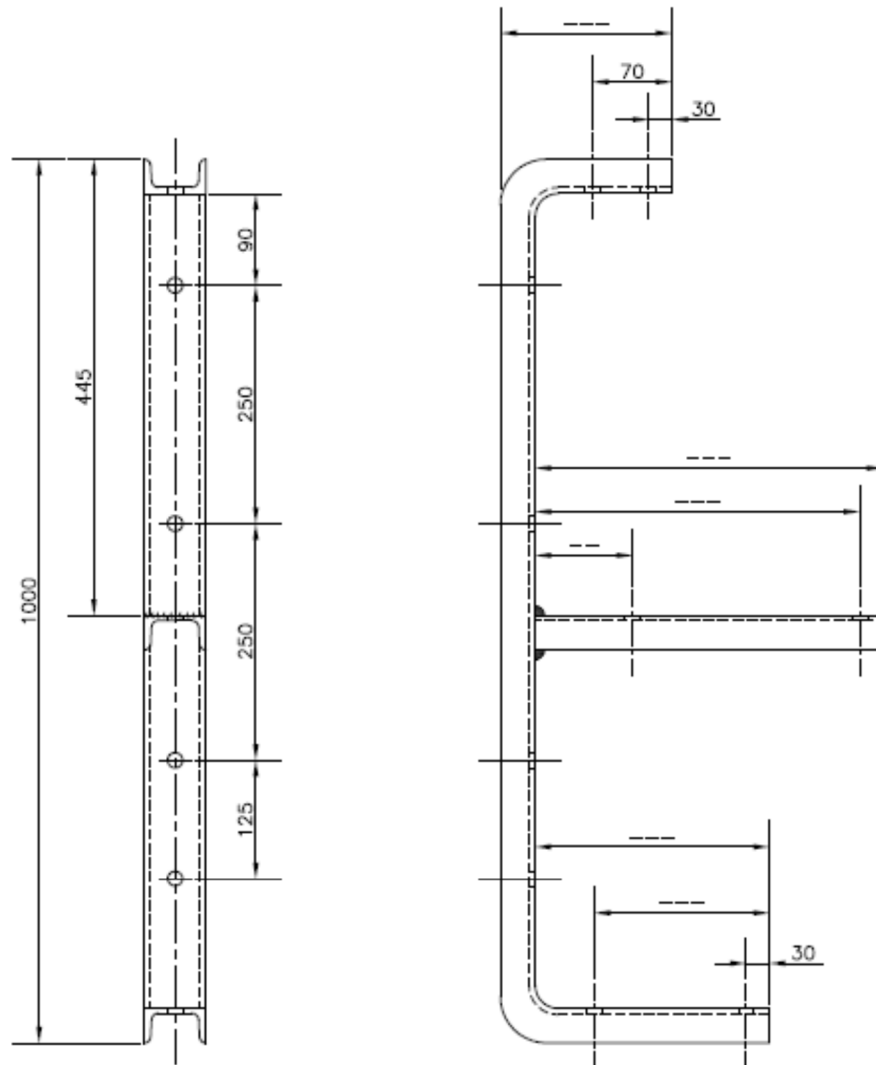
Fundações de apoio 600/250 14 [17].
